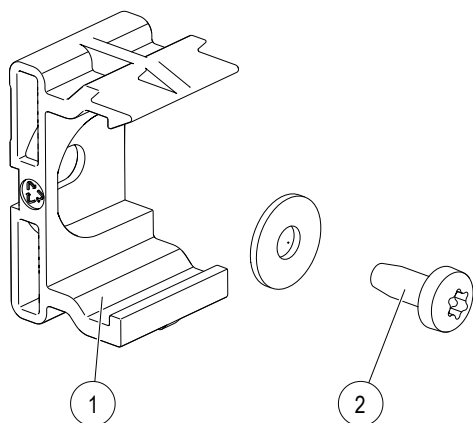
Schienenhalter mit selbstfurchender Schraube
